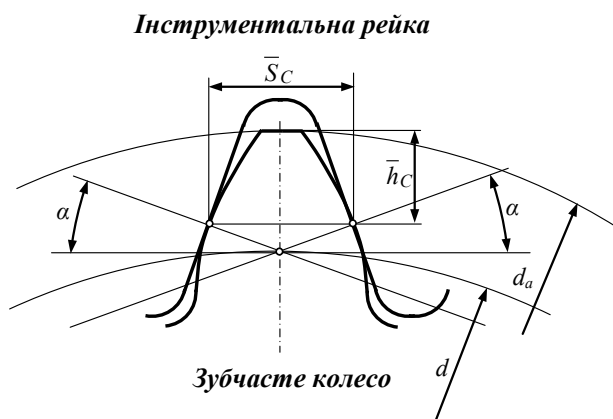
Схема вимірювання постійної хорди для зубчатих коліс із зовнішніми зубцями
